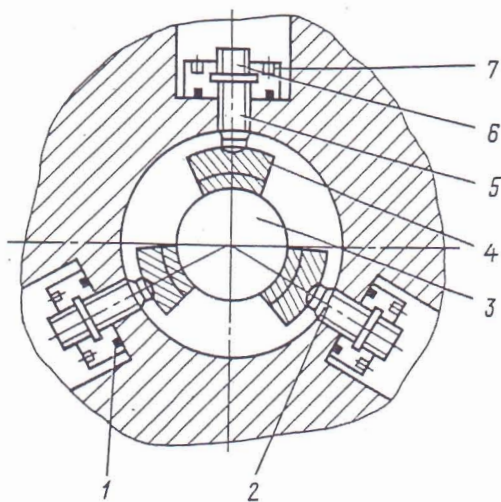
Регулирование зазоров в подшипниках шпинделя (задняя опора) для станков ЗЕ71ВФ1, ЗЕ71АФ1, ЗЕ72АФ1-1
